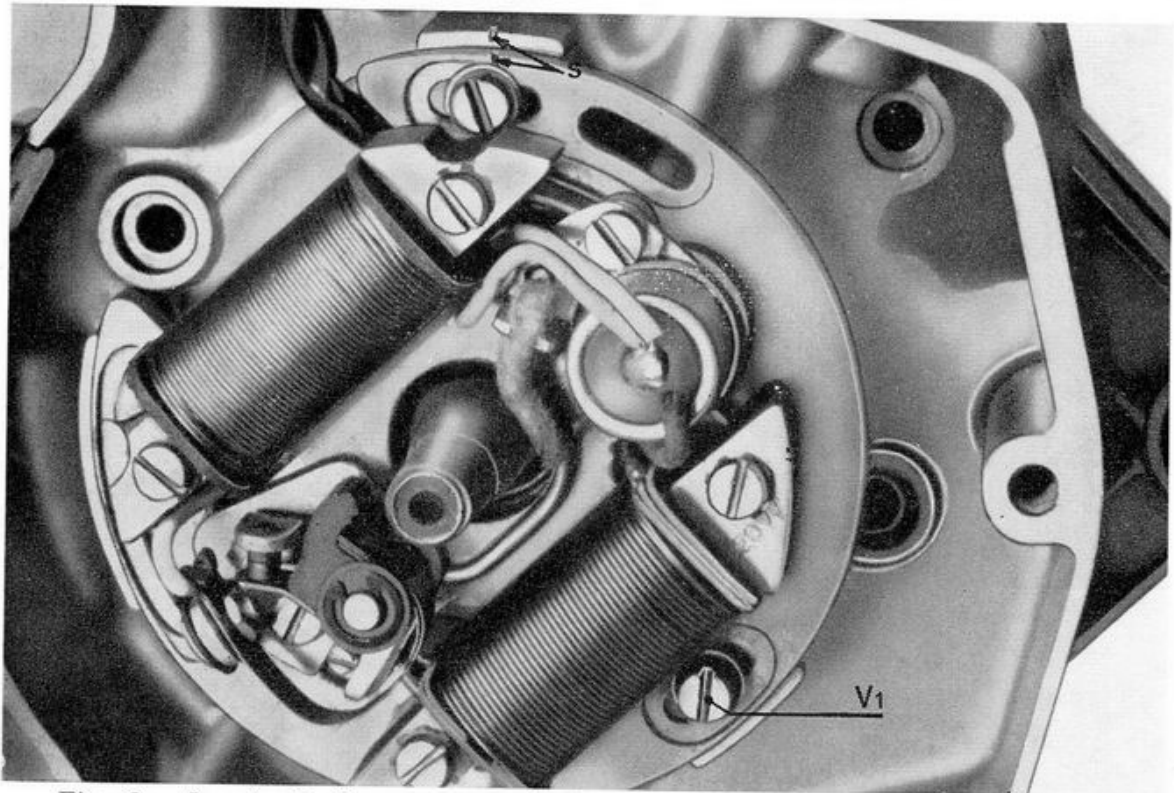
Segni di riscontro tra la basetta portabobine e il carter motore
